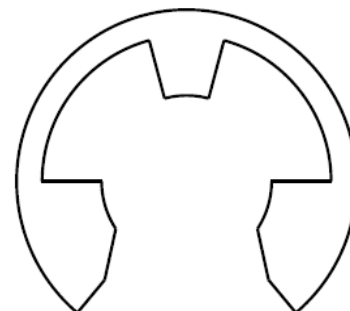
Manipulátor pro odebrání a zakládání pojistného kroužku
